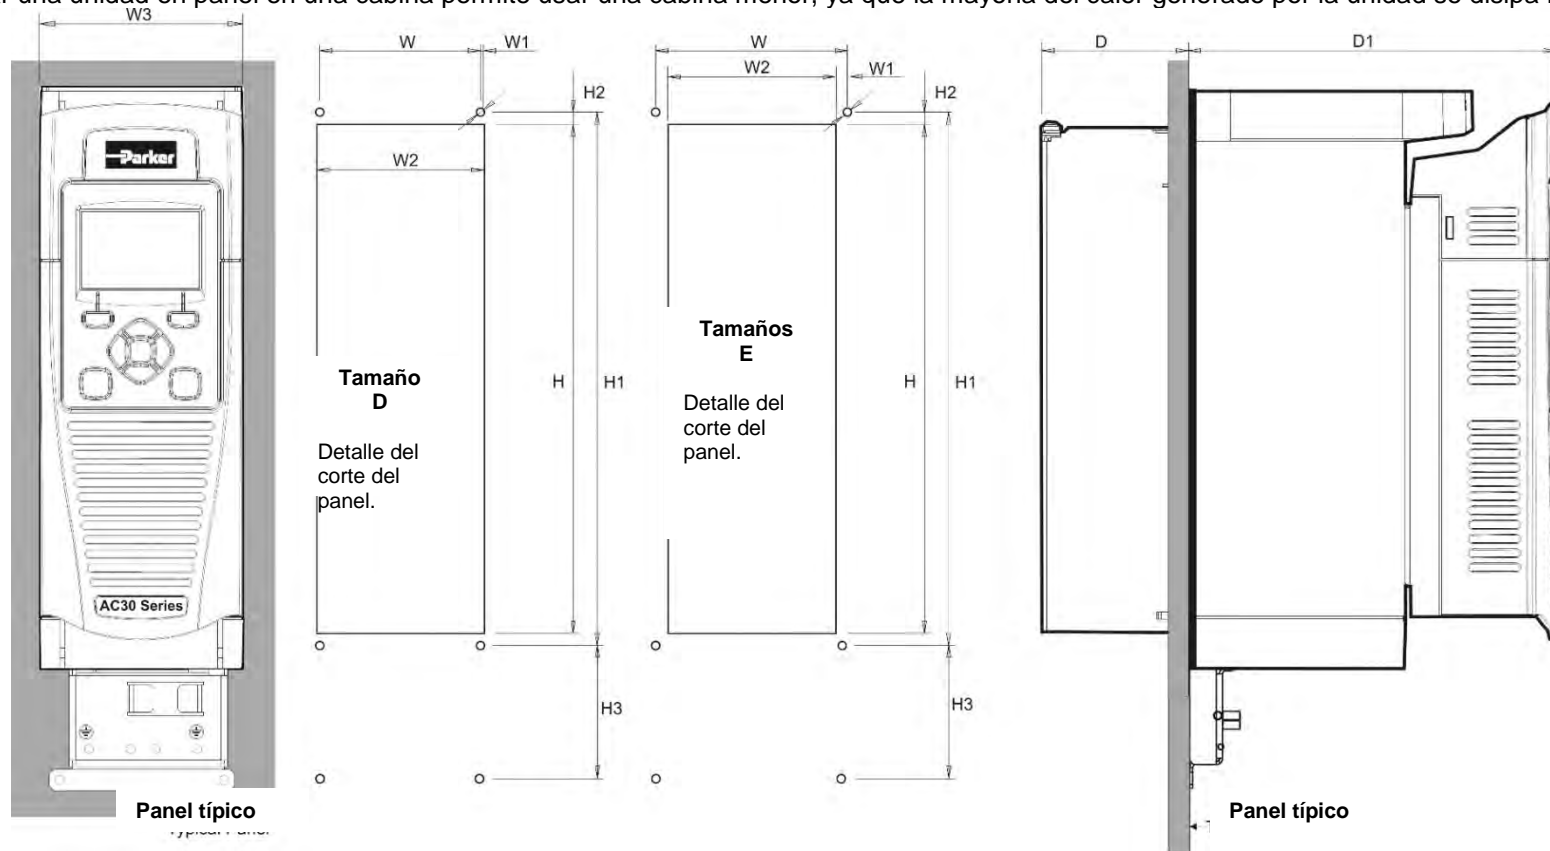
Dimensiones mecánicas de la unidad AC30 de montaje en panel - Tamaños D, E
